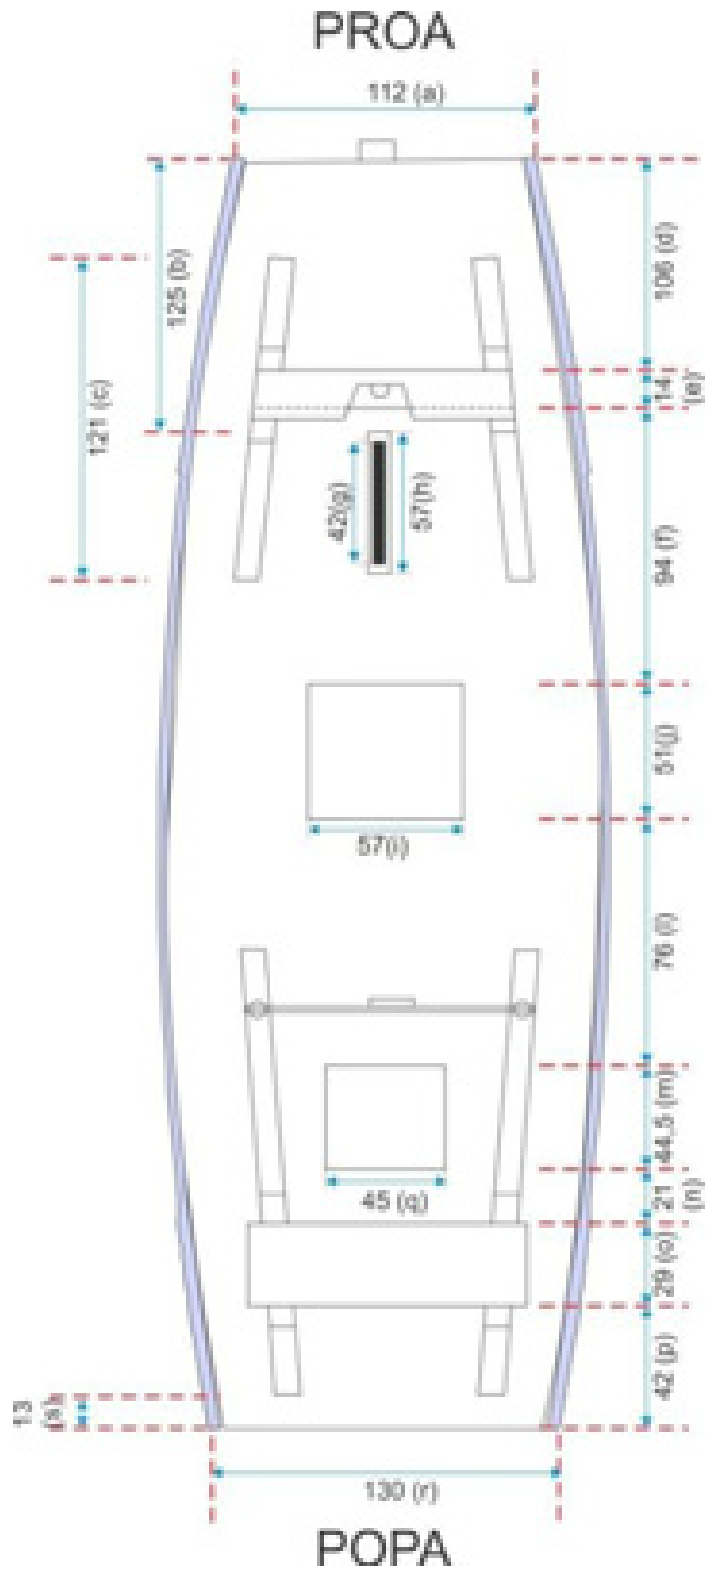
Dimensões da jangaça com melhor distribuição de espaço (vista superior) na opinião dos jangadeiros
